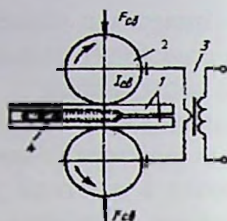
Схема шовной контактной сварки:
